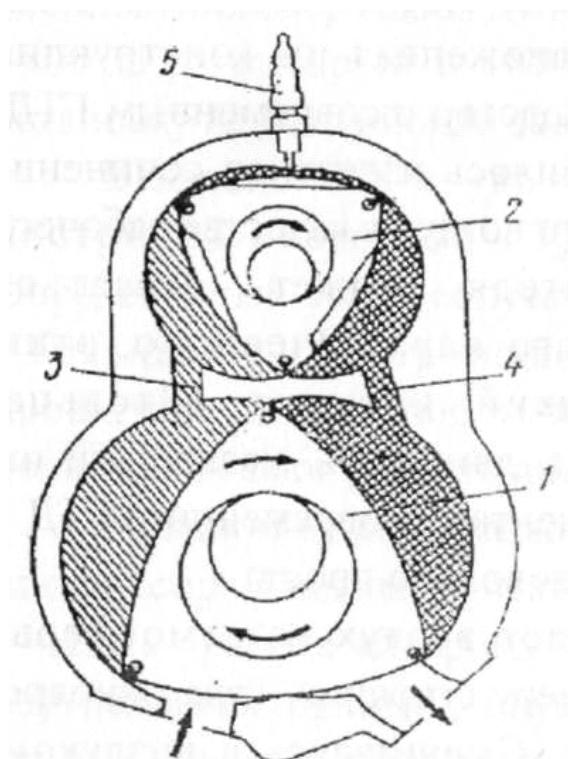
Дизель с разделённым двухстадийным сжатием и двухстадийным расширением: 1 - поршень низкого давления; 2 - поршень высокого давления; 3 - впускной перепускной канал; 4 - выпускной перепускной канал; 5 - впрыскивающая форсунка
